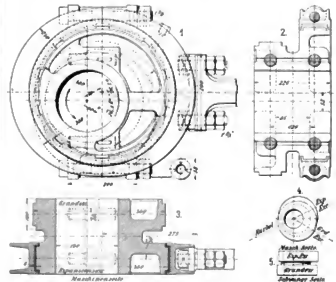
Z. A.: Eine Heißdampf-Tandemmaschine.
